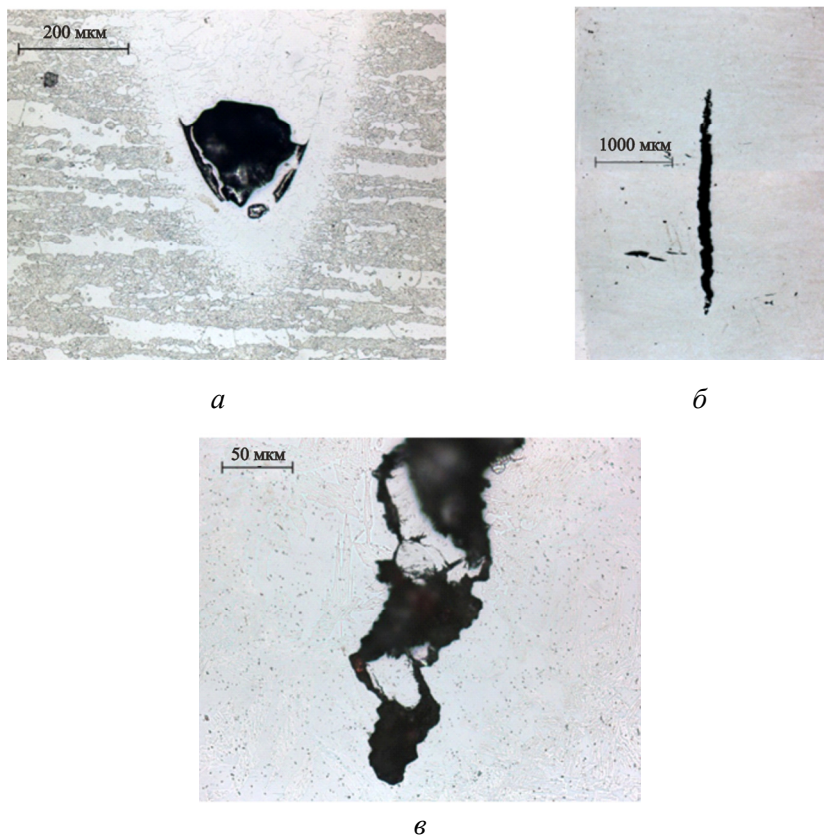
Дефекты сварных соединений сталей 09X17H-Ш и 08X18H10T, выполненных ЭЛС: *а* – корневой дефект в образце 1; *б* – трещина в металле шва по центру в образце 4.1; *в* – вершина трещины (см. рис. 3, б)
